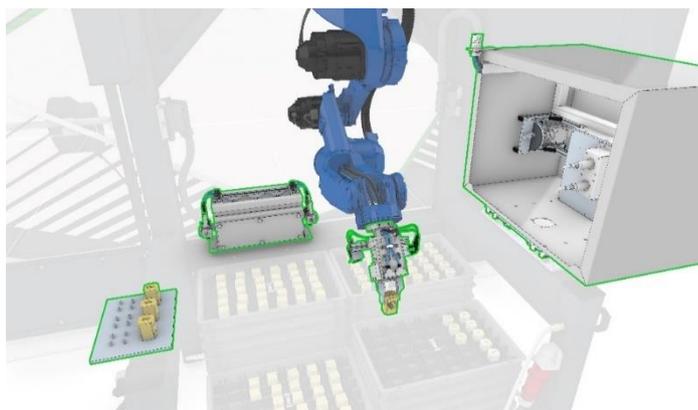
Einsatz des »Robo Operators« an einer Werkzeugmaschine (Simulation; Quelle: IP)
